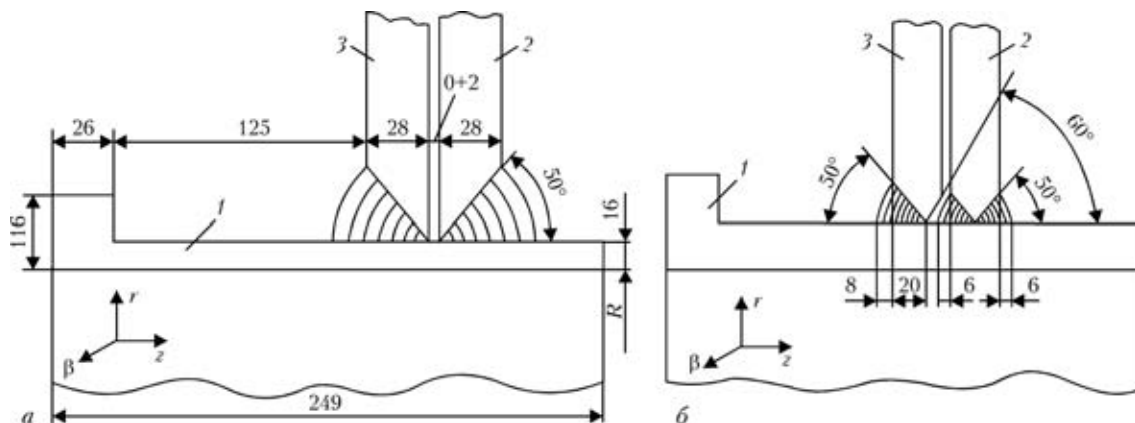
Схема сварного соединения (поперечное сечение сварного шва) патрубка со стенкой и накладным листом зачистного люка резервуара: *а, б* — соответственно вариант № 1, № 2; 1–3 — см. в тексте
